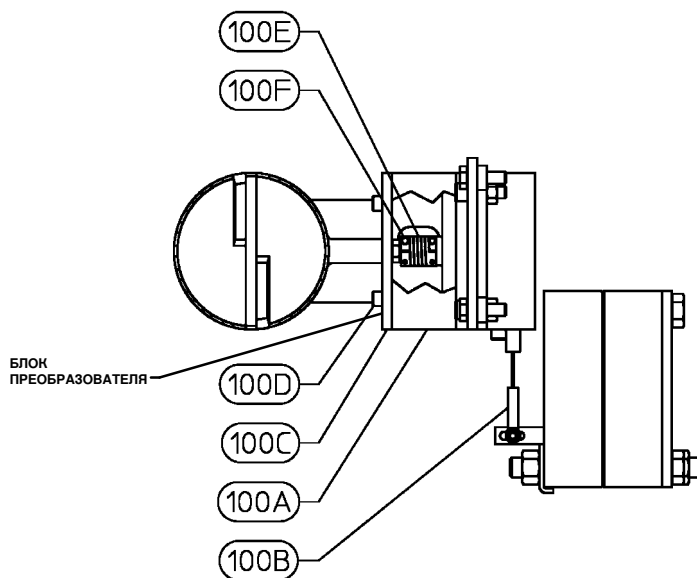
Обычное крепление датчика на приводах Fisher® 585CLS (490)
